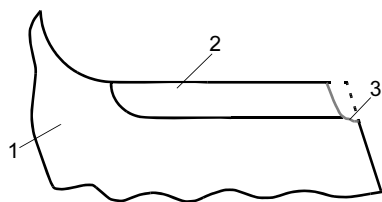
Повреждение малого зуба корпуса автосцепки: 1 — основной металл; 2 — наплавленный слой; 3 — поврежденный участок
